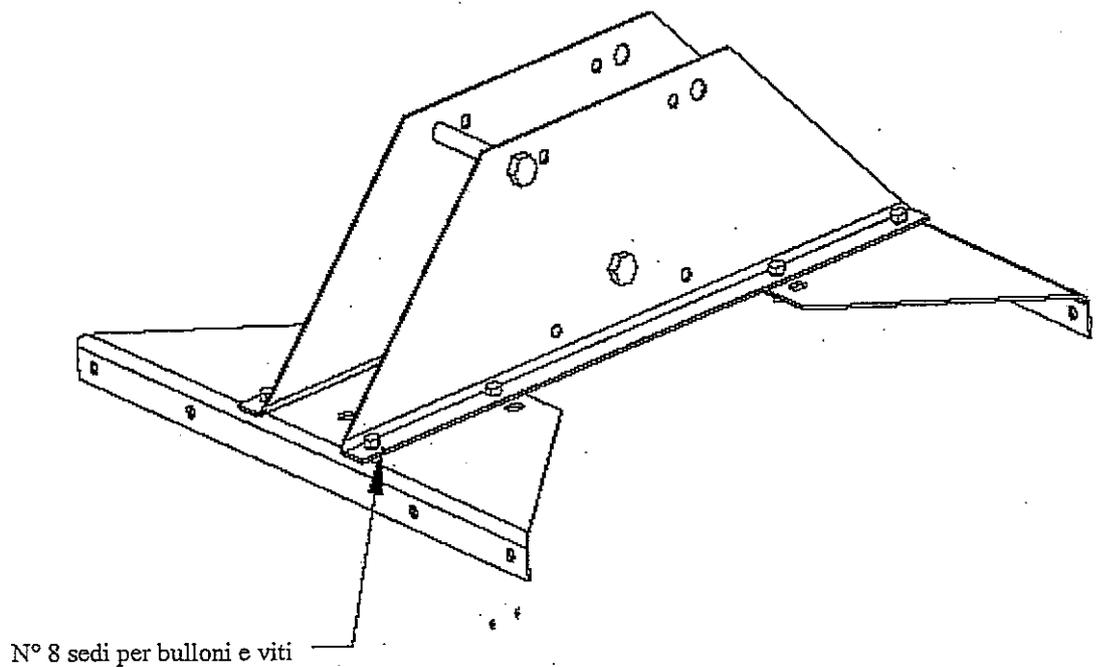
Sostegno di base del palo, che consente la rotazione per il sollevamento.
